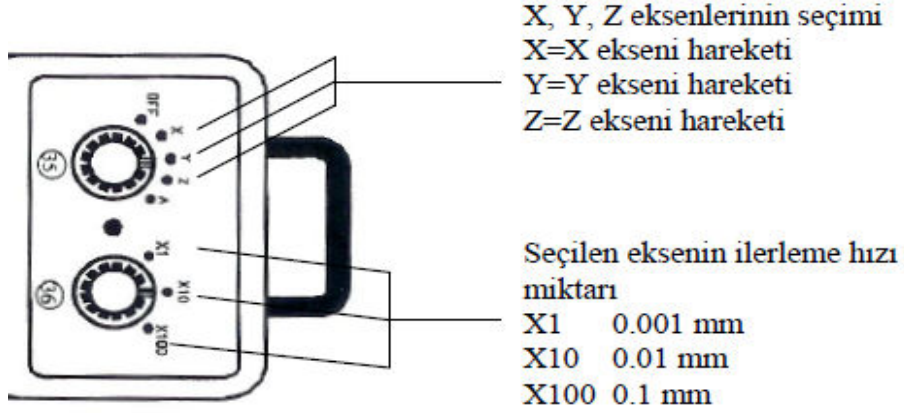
Siemens kontrol ünitesinde el çarkının devreye alınması işlem basamakları
